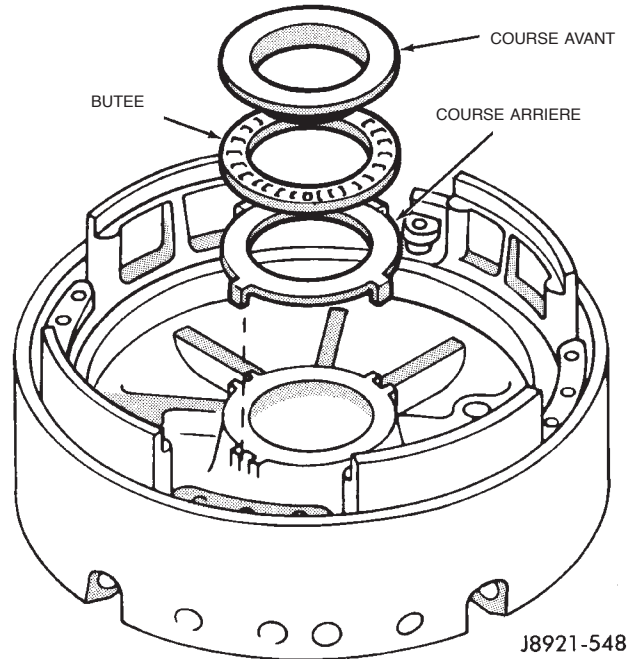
Pose de l'ensemble de roulement de course de tambour d'embrayage
